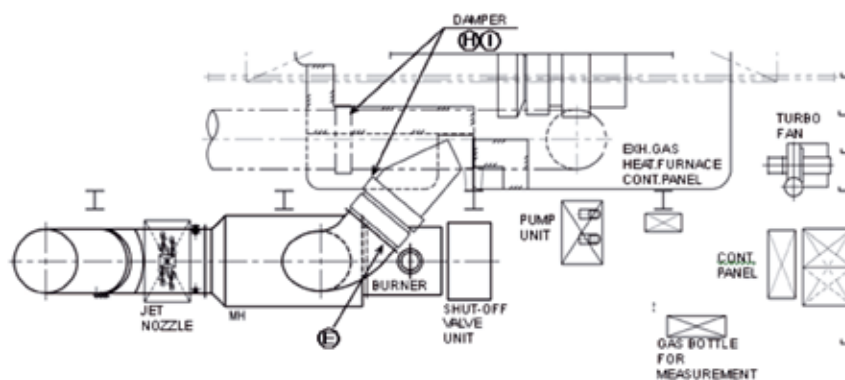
SCR 装置配置概要図 (2ND DK 平面図)
